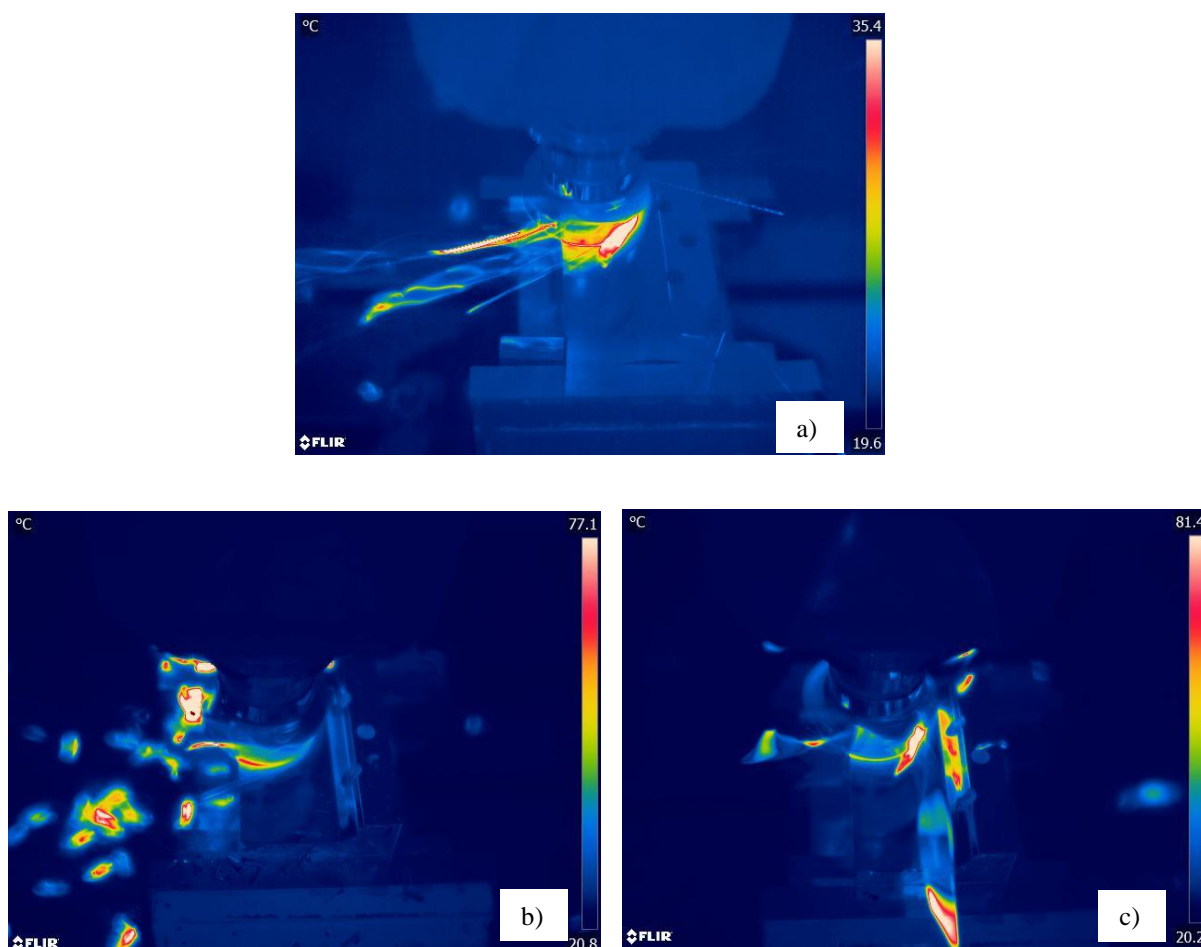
Termogramas de usinagem a) $v_c = 100$ m/min; $f_z = 0,05$ mm/aresta; $a_p = 0,5$; seco; inserto cermet b) $v_c = 150$ m/min; $f_z = 0,1$ mm/aresta; $a_p = 1$; seco; inserto cermet e c) $v_c = 100$ m/min; $f_z = 0,05$ mm/ aresta; $a_p = 1,5$; seco; cermet.
